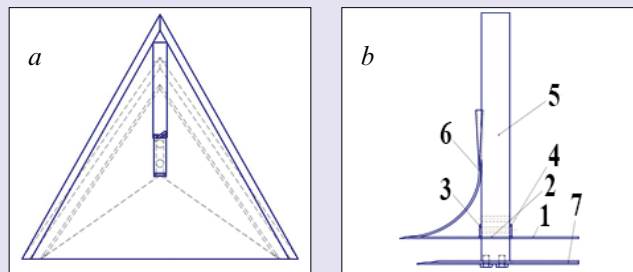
Схема двухъярусной стрелчатой почвообрабатывающей лапы:
